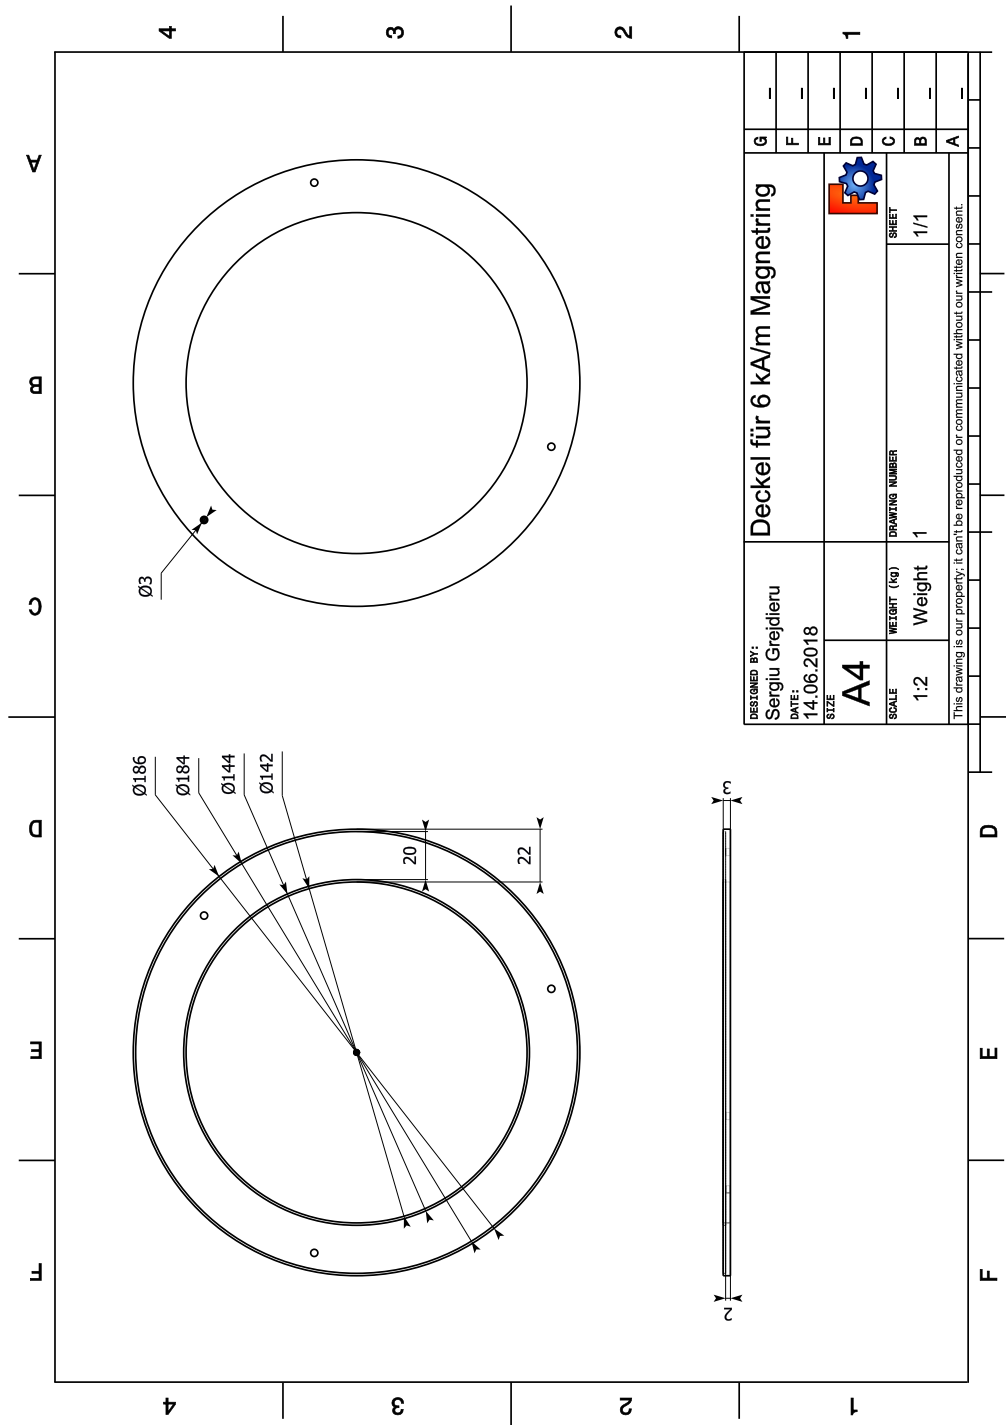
Technische Zeichnung: Deckel für Magnetring 6 kA/m
